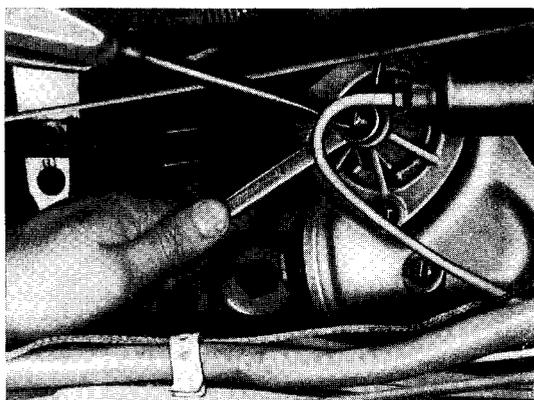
Einstellschraube aus Lenkgehäusedeckel bis zum Anschlag herauszuschrauben
